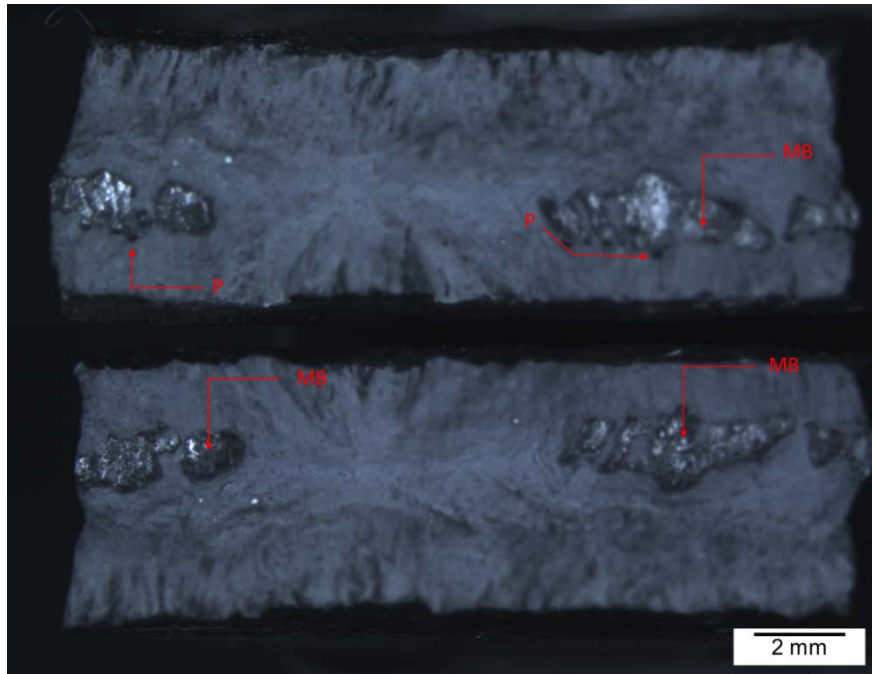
Imagen por estereoscopio de la fractura del ensayo de tensión T1 unión soldada ER-308L.
